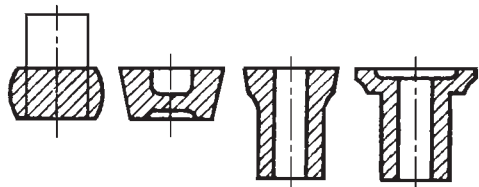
Схема четырехпереходной (считая осадку) штамповки поковки с наметкой и прошивкой сквозной полости
